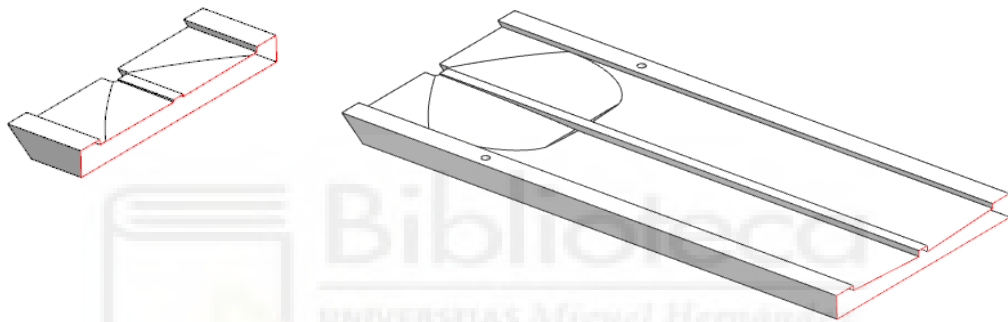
Placa de PE 1000. Conjunto de rotación. Mecanizado CNC. Detalle de secciones.
